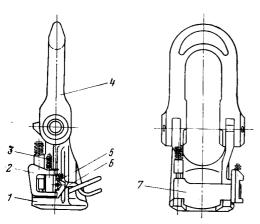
Элеватор трубный ЭГ: 1— корпус: 2— защелка; 3— пружина защелки; 4— штроп; 5— пружина фиксатора; 6— фиксатор; 7— створка
